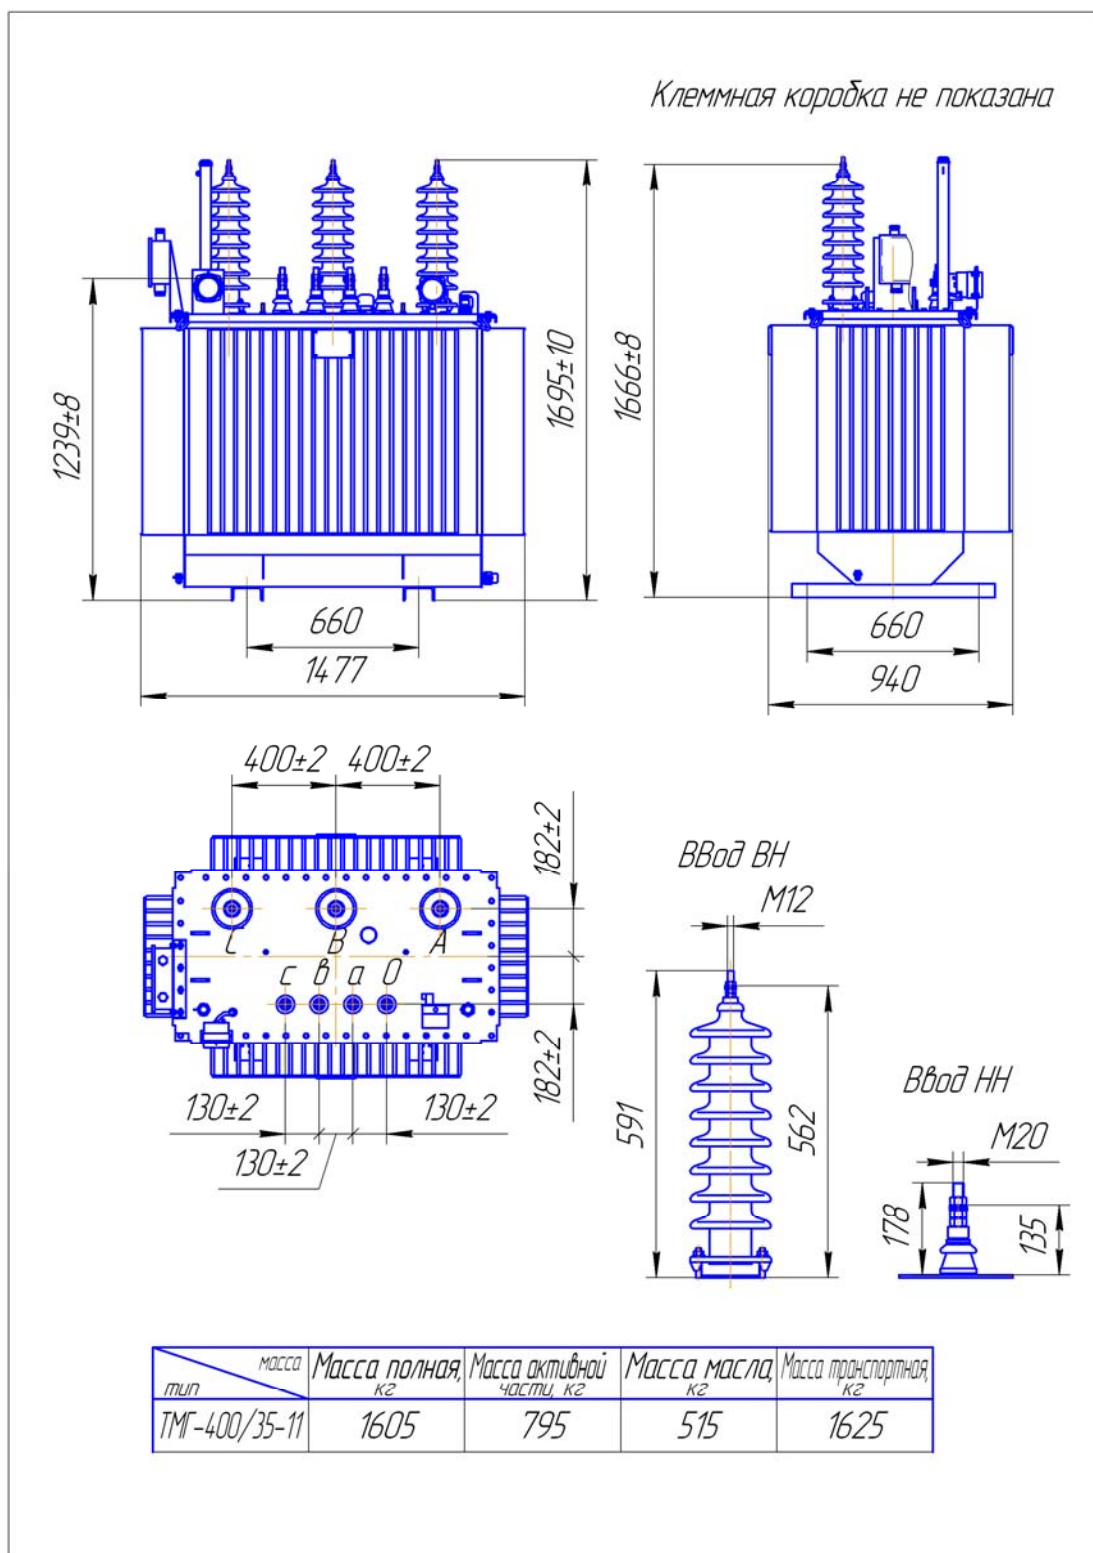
Габаритные, установочные и присоединительные размеры трансформатора ТМГ - 400/35-11
